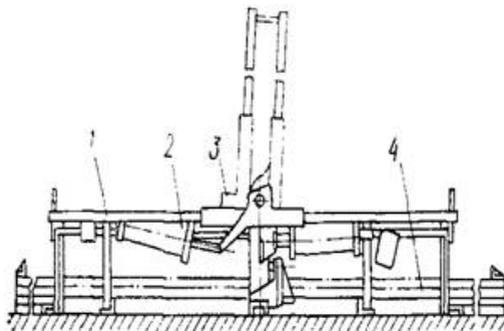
Кантователь книжный: 1 – поворотная рама; 2 – привод поворота; 3 – механизм крепления изделия; 4 – станина
